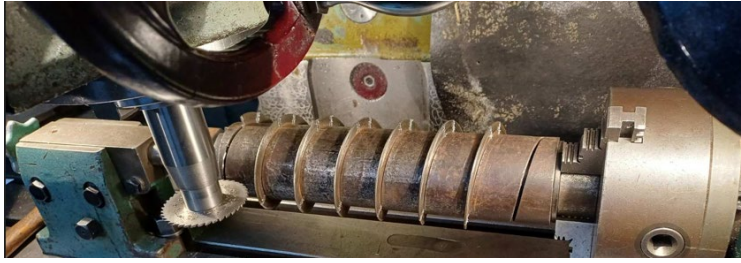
Загальний вигляд розрізання зовнішньої крайки спіралі шнека для отримання заготовок під ножі-подрібнювачі
